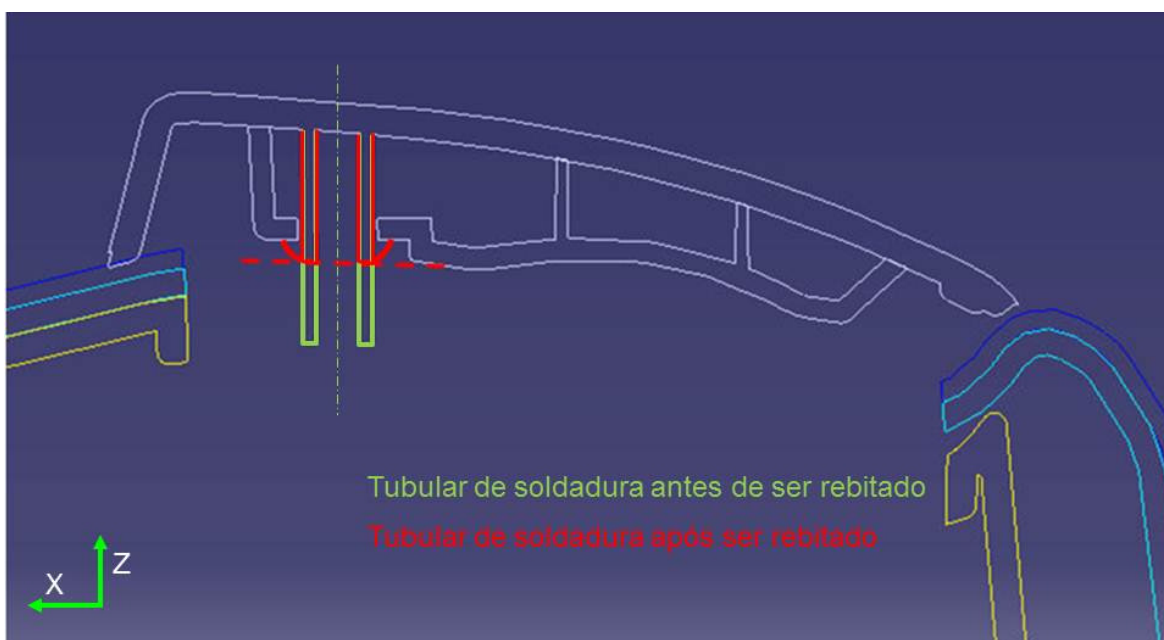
Secção da zona de soldadura dos 'Deckels Outer' com os 'Inner'
